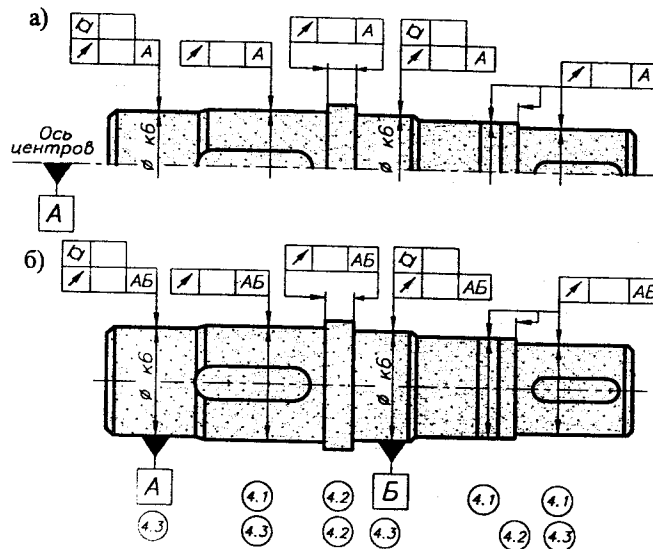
Обозначение допусков формы и расположения поверхностей вала, когда:
